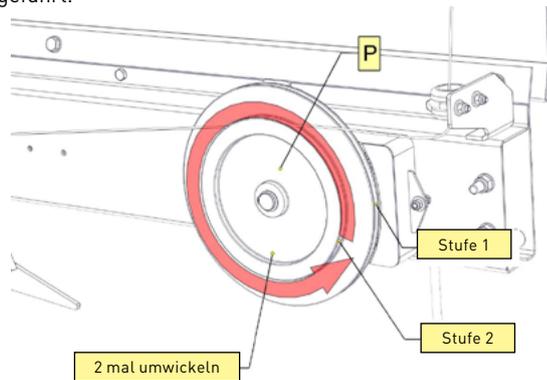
Einstellung der Wickeldichte der Ballen mit dem Seil
